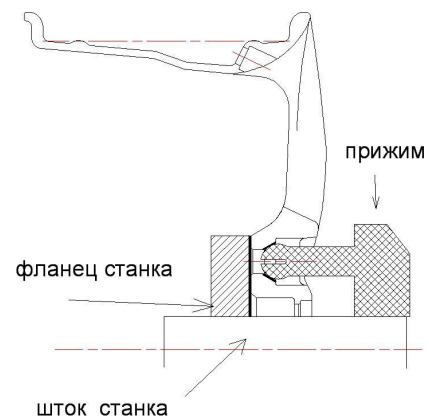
Закрепление колеса по привалочной плоскости и крепежным отверстиям (очень редкий случай)
